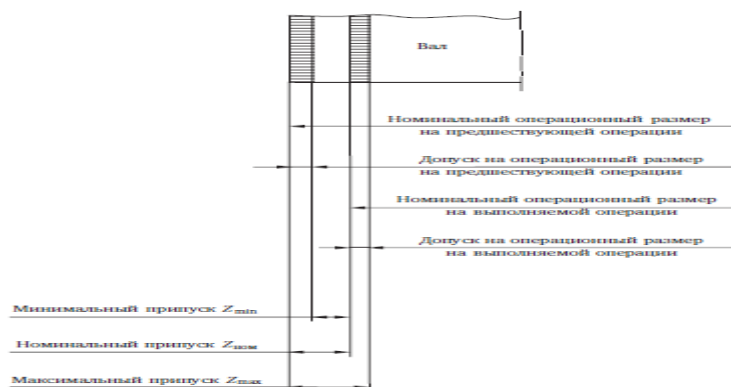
Схема расположения операционных припусков и допусков при обработке наружной цилиндрической поверхности (вала)
